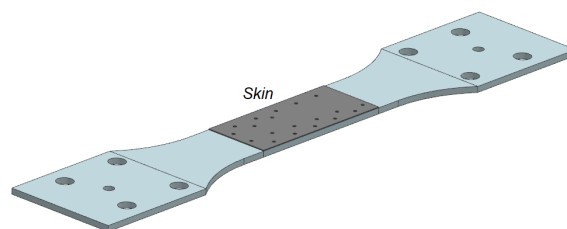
Configuração do provete com a *skin* e elementos de ligação
